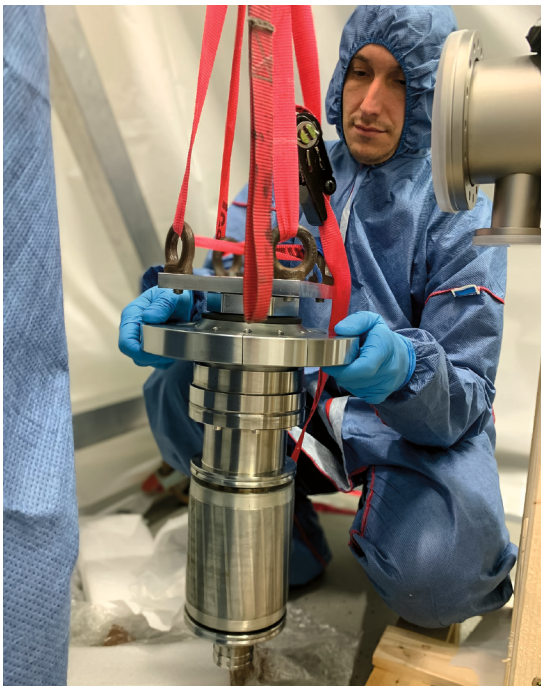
Montage der Anodendrehbaugruppe mit dem Motor durch das muFlash-Team
